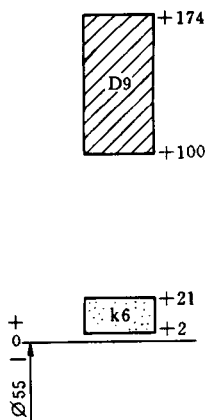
轴套孔与轴颈的公差带示意图
